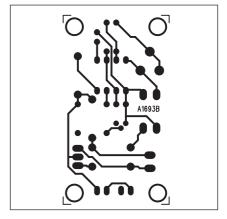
Obrazec desky spojů zdvojovače (strana TOP)
